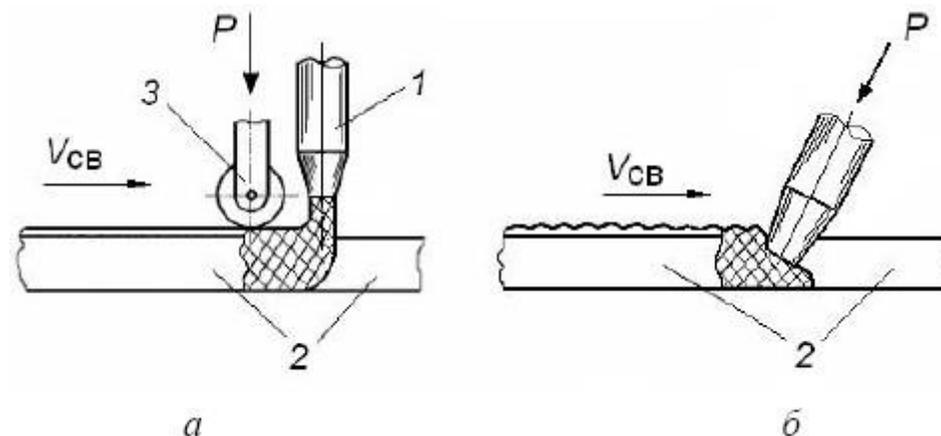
Схемы бесконтактной (а) и контактно-экструзионной (б) сварки расплавом: 1 – мундштук экструдера; 2 - свариваемые детали; 3 – прикатывающий ролик
